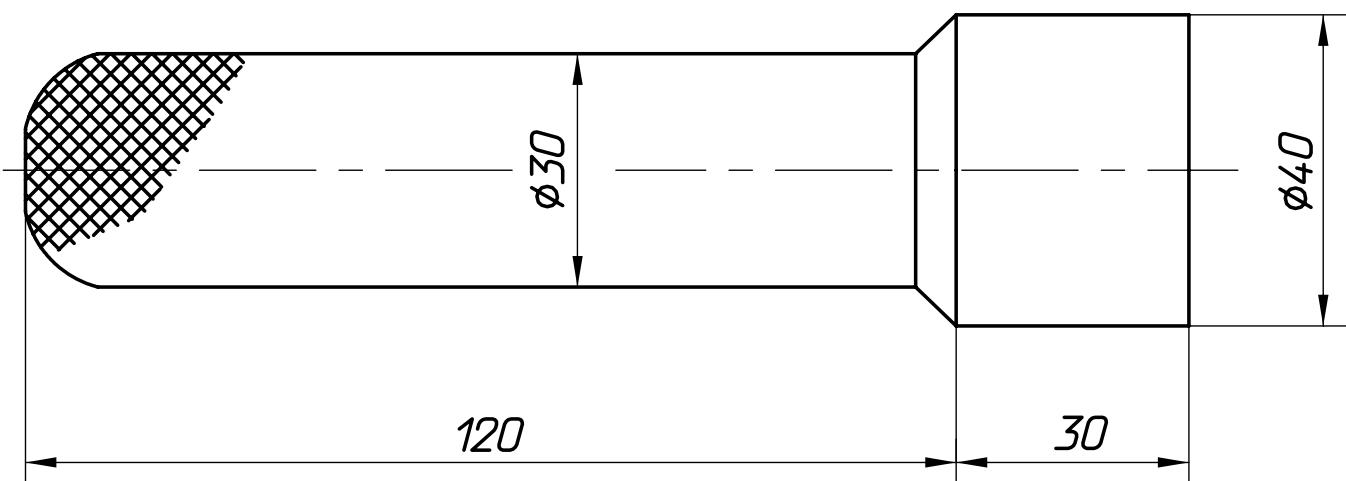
Оправка для выпрессовки теплопередающего элемента
